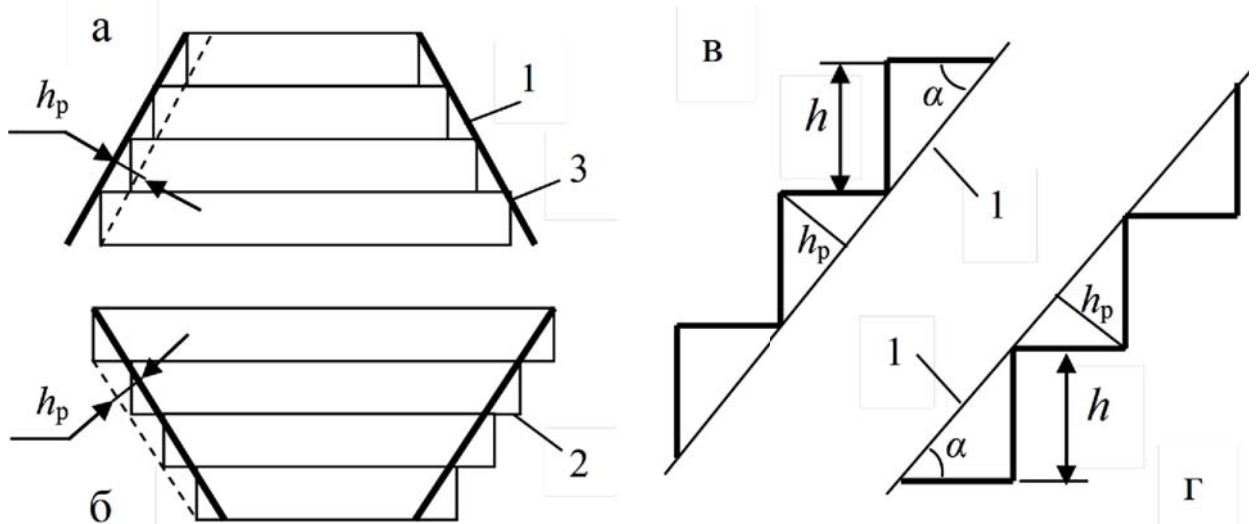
Варианты формирования ступенчатого рельефа на поверхности шестерни: вариант 1 (а, в) и вариант 2 (б, г); 1 – CAD-поверхность спроектированной шестерни; 2 – ступенчатый рельеф изготовленной шестерни; 3 – листовые выкройки (наращиваемые слои)
